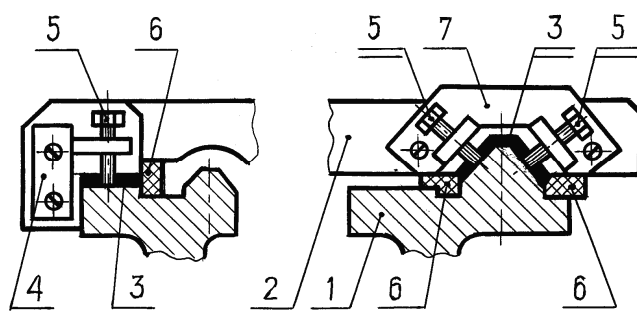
Формирование восстанавливающего слоя «Моглайс» на направляющих поверхностях салазок суппорта: 1 – станина; 2 – салазки суппорта; 3 – слой материала «Моглайс»; 4 – левый уголок; 5 – регулировочный винт; 6 – уплотнение; 7 – правый уголок
